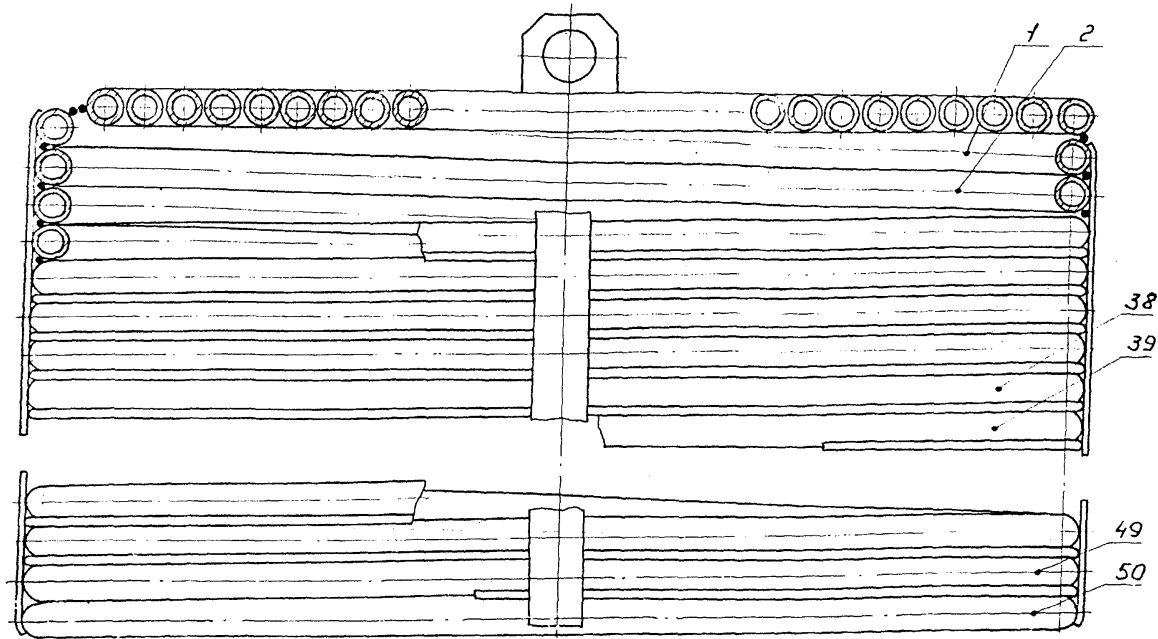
Схема контроля сварных швов спирали
